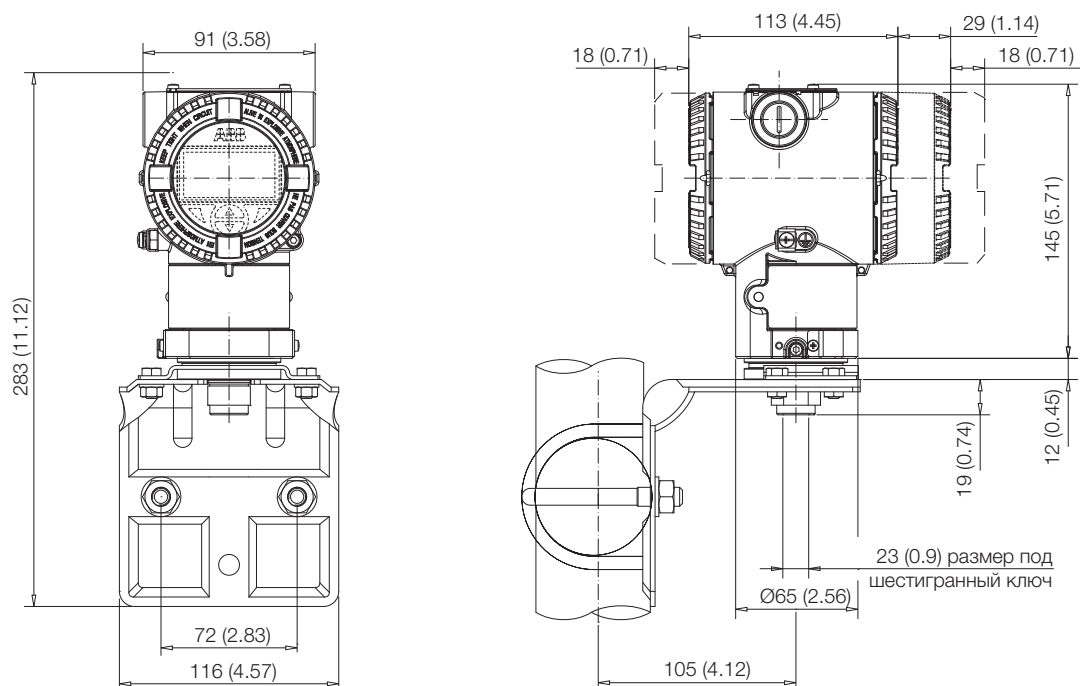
Модель 266N или P-образный, устойчивый к перегрузкам датчик 266N с измерителем Z с цилиндрическим корпусом, установленный на двухдюймовой трубе с помощью дополнительного кронштейна (B6 - углеродистая сталь или B7 - нержавеющая сталь 316L)
